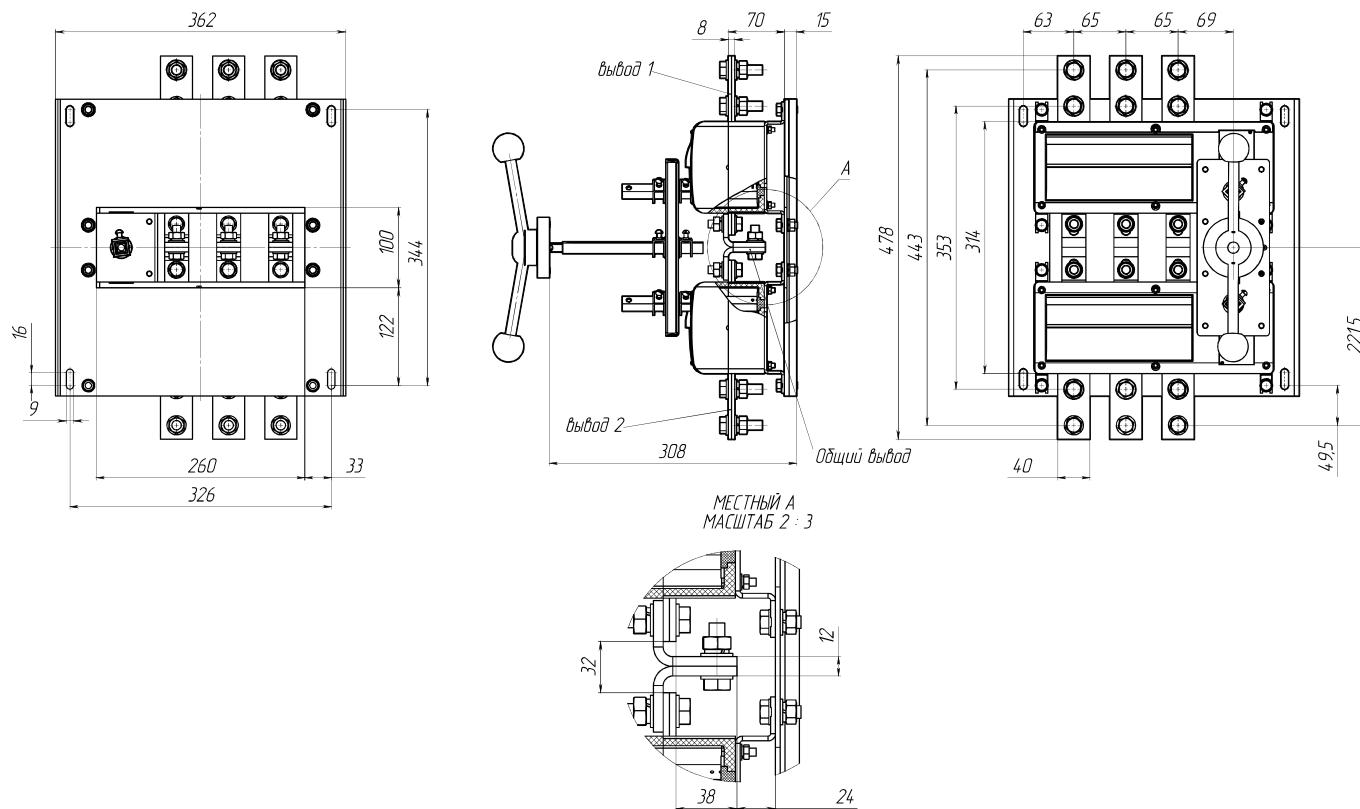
Выключатель-разъединитель ВНК-39-71130-32 УХЛ3 на два направления, масса не более 14,5 кг
